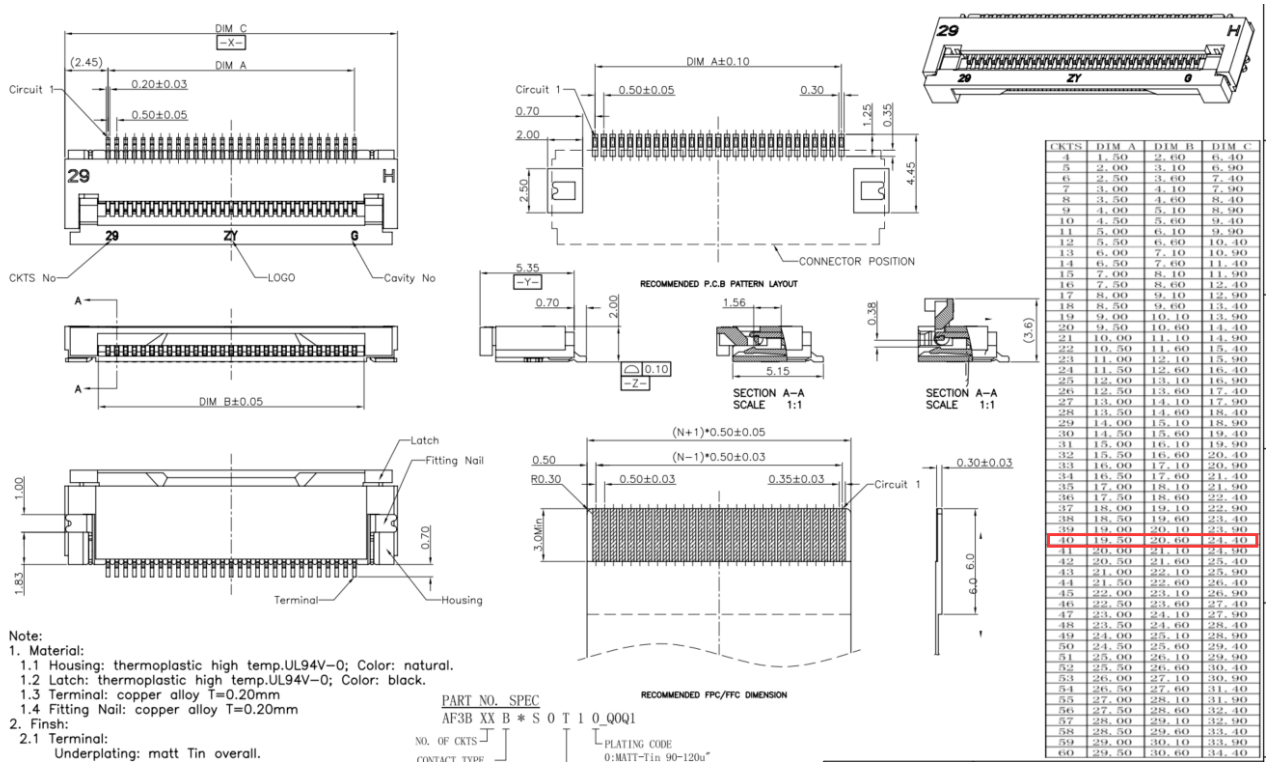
间距 0.5mm 翻盖式 40 PIN FPC PCB 封装
